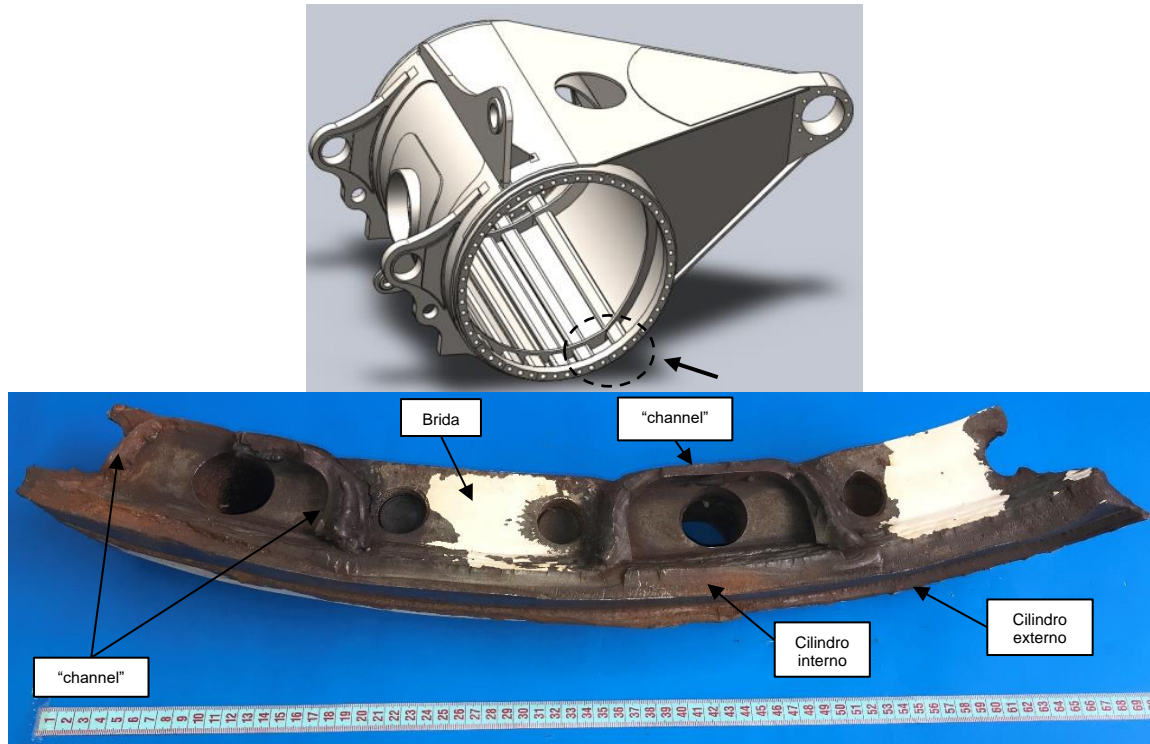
Detalles de construcción, unión “channel”-Anillo refuerzo interno.
